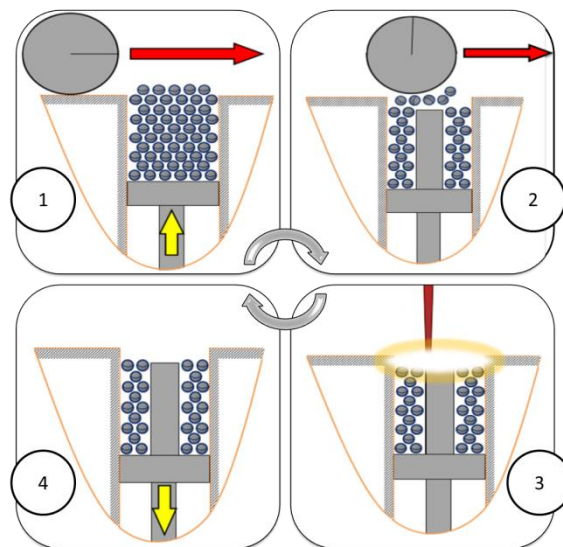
Principe de fabrication d'un objet par procédé LBM. (1) montée du piston d'alimentation, (2) étalement de la poudre sur le haut de la pièce en construction, (3) fusion sélective du lit de poudre et (4) descente du piston de fabrication
